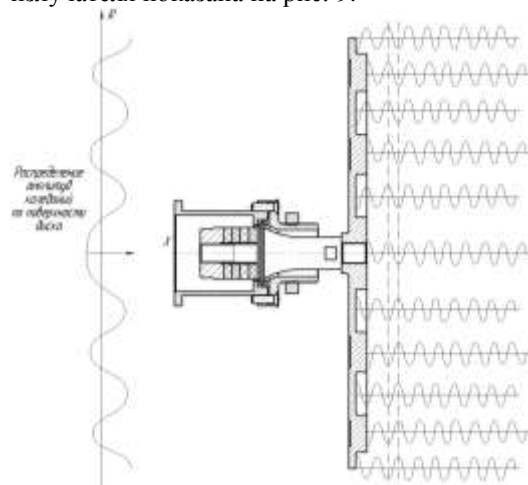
Схема излучателя с фазовыравнивающими элементами
